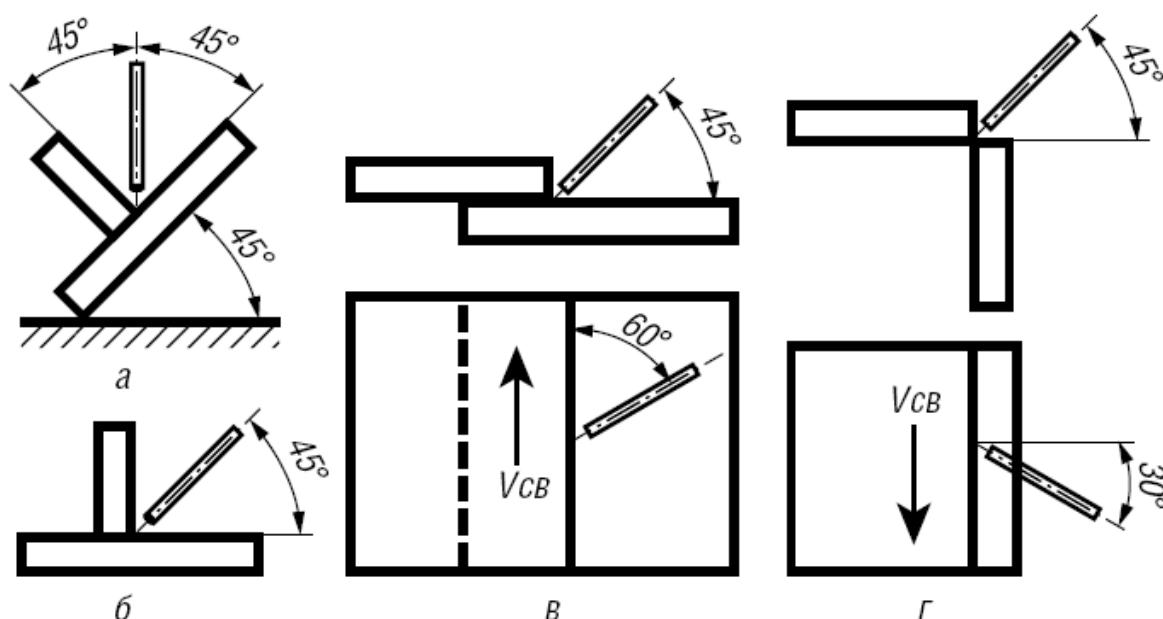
Схема сварки стыковых швов:
